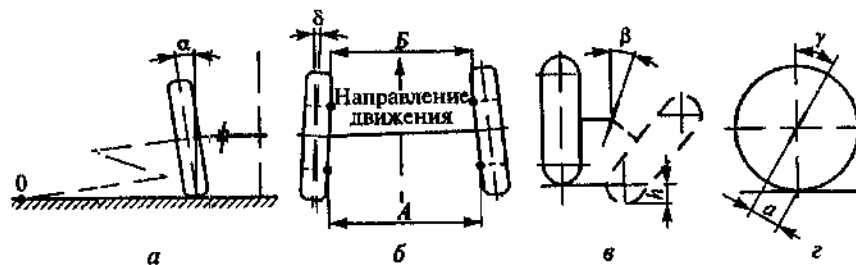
Схемы установки (а, б) и стабилизации (в, г) управляемых колес автомобиля:
